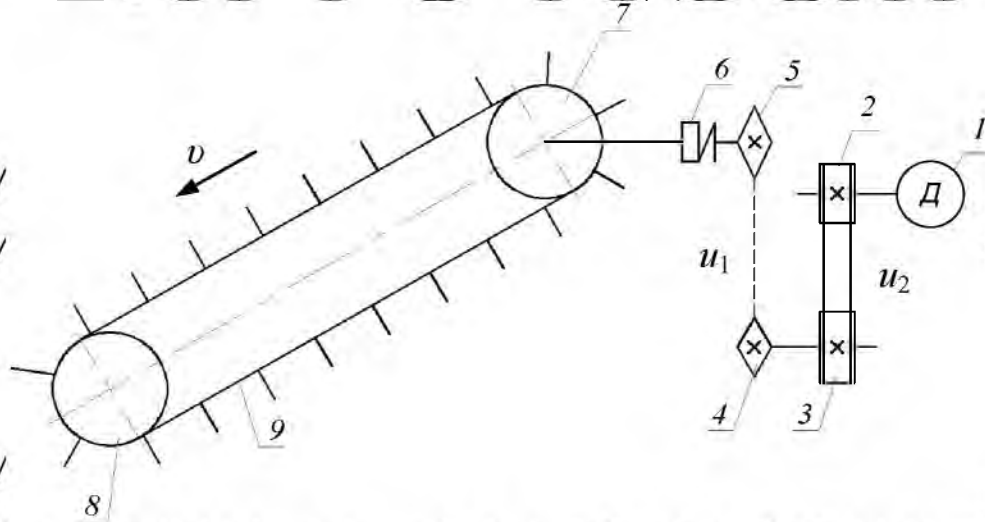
Кінематична схема скребкового конвеєра: 1 – двигун; 2, 3 – шківни пасової передачі; 4, 5 – зірочки ланцюгової передачі; 6 – муфта; 7 – приводна зірочка; 8 – приводна зірочка скребкового конвеєра; 9 – ланцюг зі скребками
